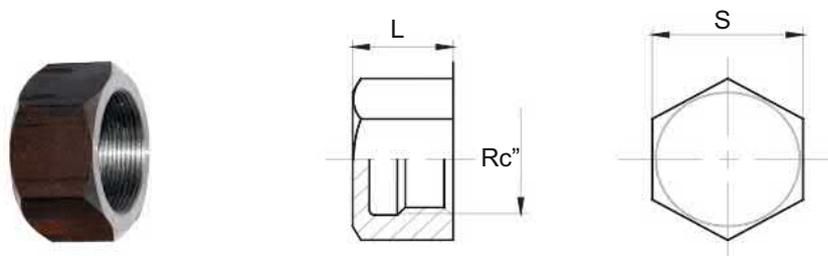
Заглушка для установки на выпускном трубопроводе на ниппели
